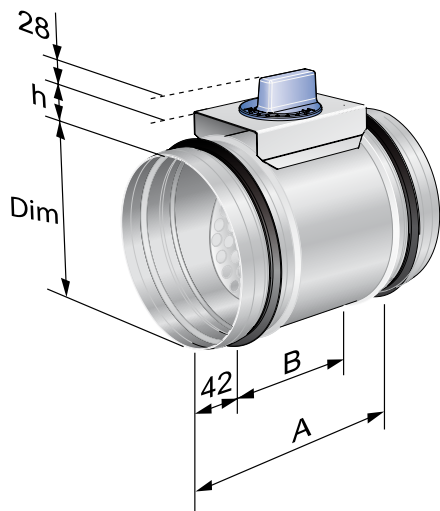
Serranda di taratura SYST CRPc 9-100, 125 o 160
